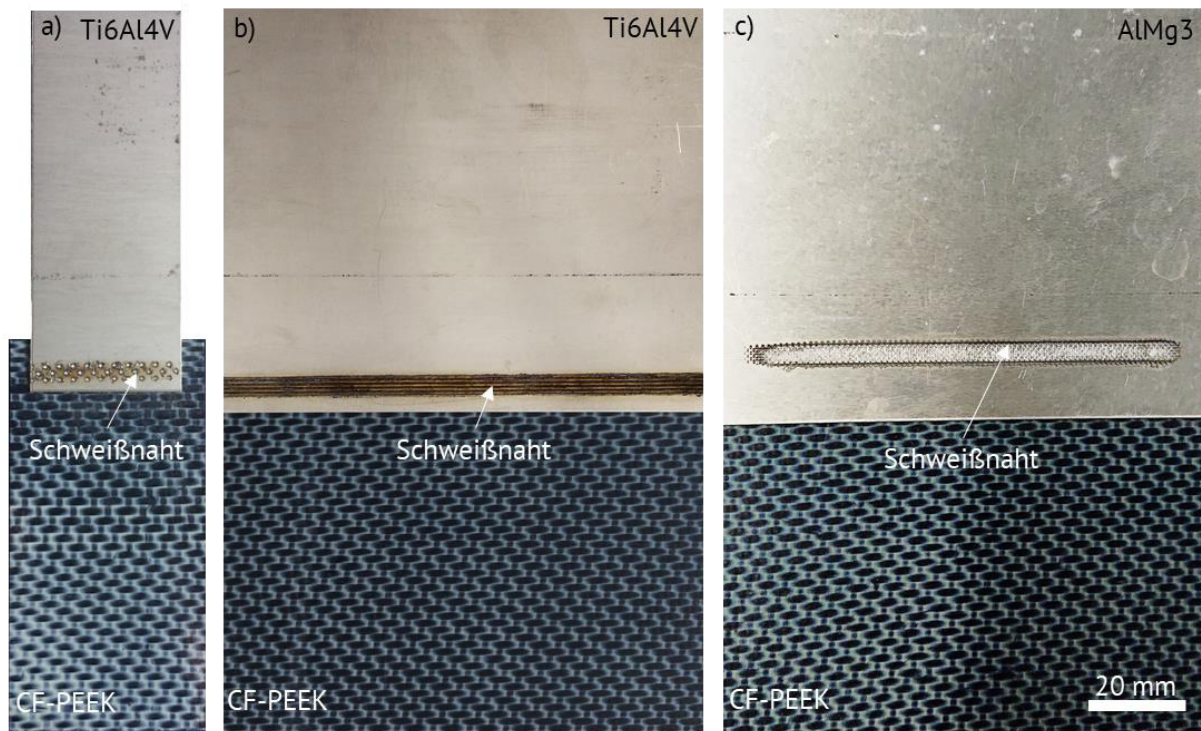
Translatorisch ultraschallgeschweißte Metall/CF-PEEK-Verbunde: a) Ti6Al4V/CF-PEEK mit 30 mm Schweißnahtlänge, b) Ti6Al4V/CF-PEEK mit 100 mm Schweißnahtlänge und c) AlMg3/CF-PEEK mit 80 mm Schweißnahtlänge.
